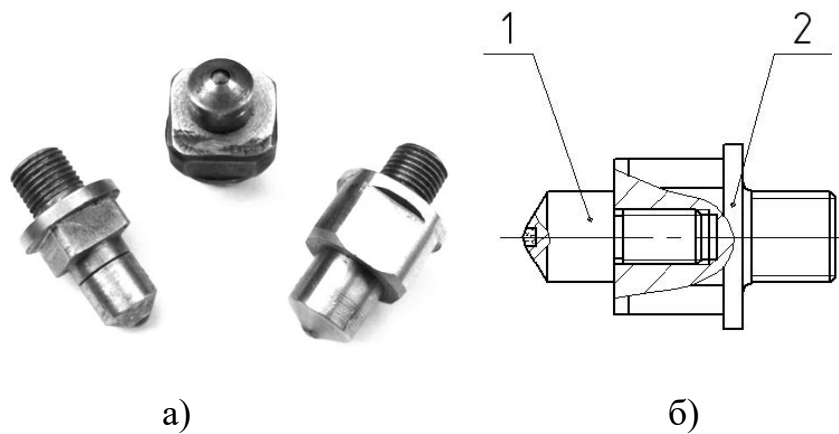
а) эскиз головки для УЗО б) сферический выглаживатель
